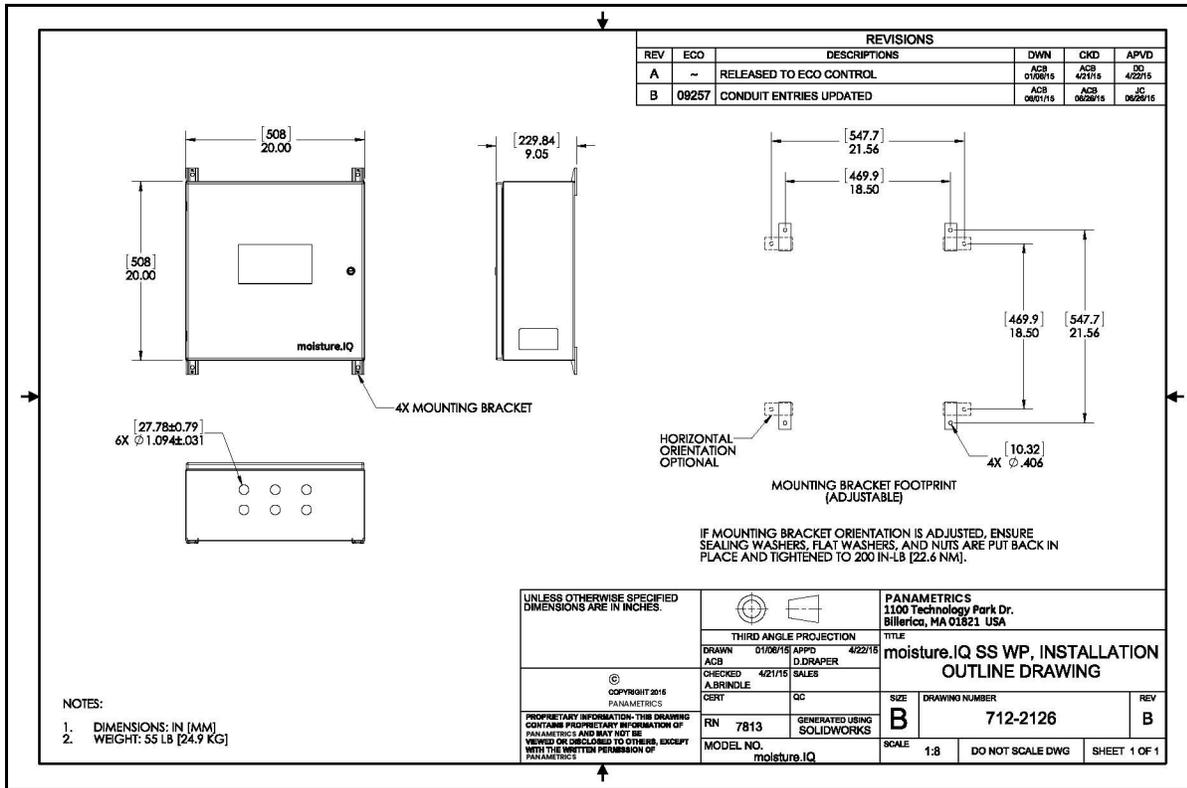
Габаритный чертеж для монтажа SS WP (чертеж 712-2126_revB, лист 1 из 1)
